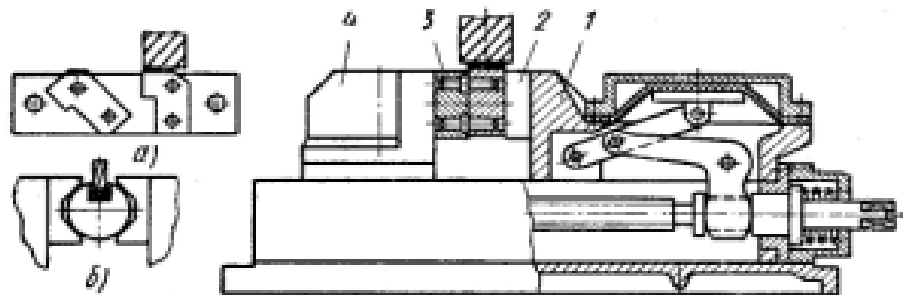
УНП з пневматичним затиском для фрезерування
